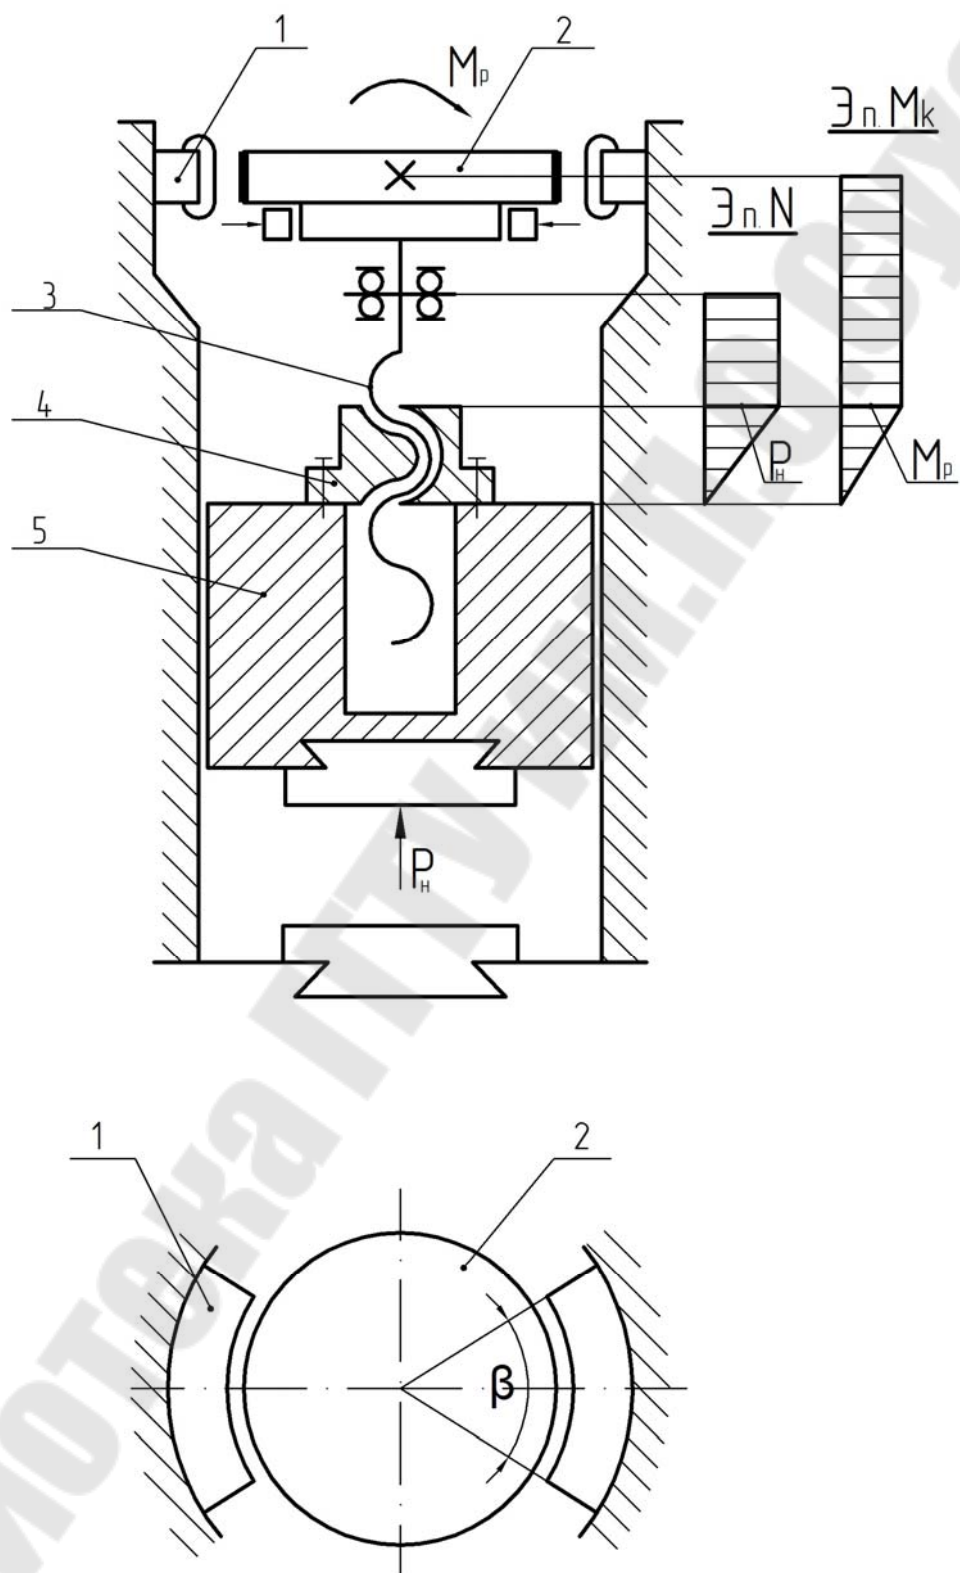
Кинематическая схема винтового прессы с дугостаторным приводом
